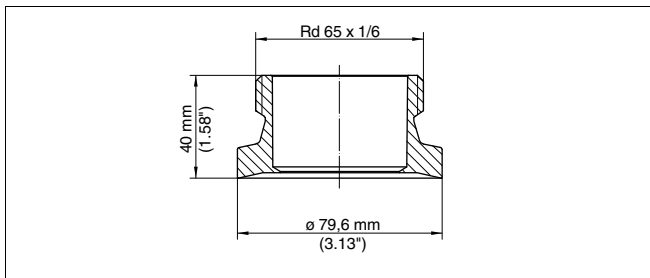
Размеры приварного штуцера LA для шлицевой накидной гайки
